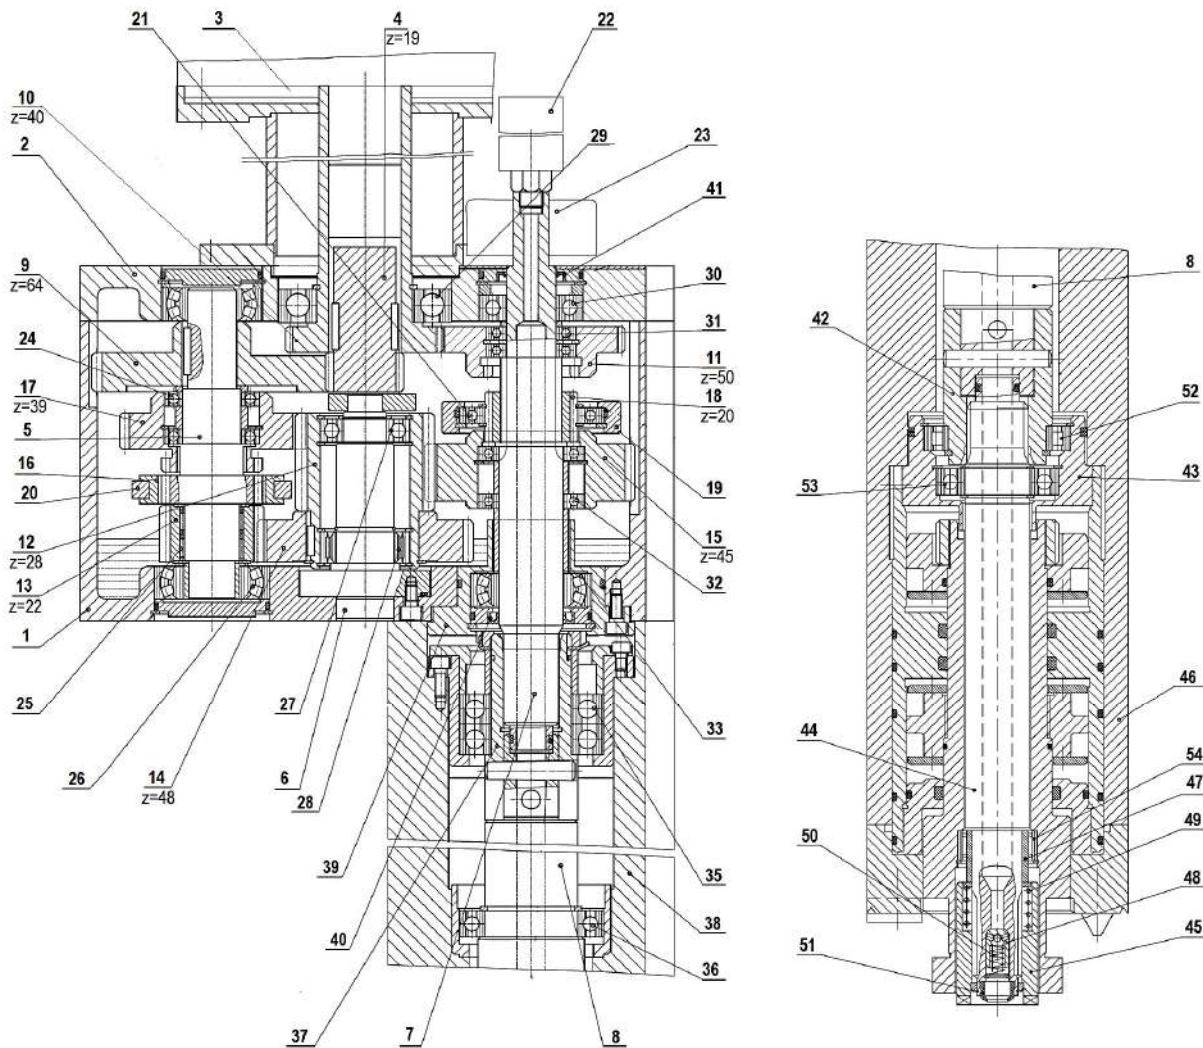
Конструкція механізму приводу обертового інструмента
